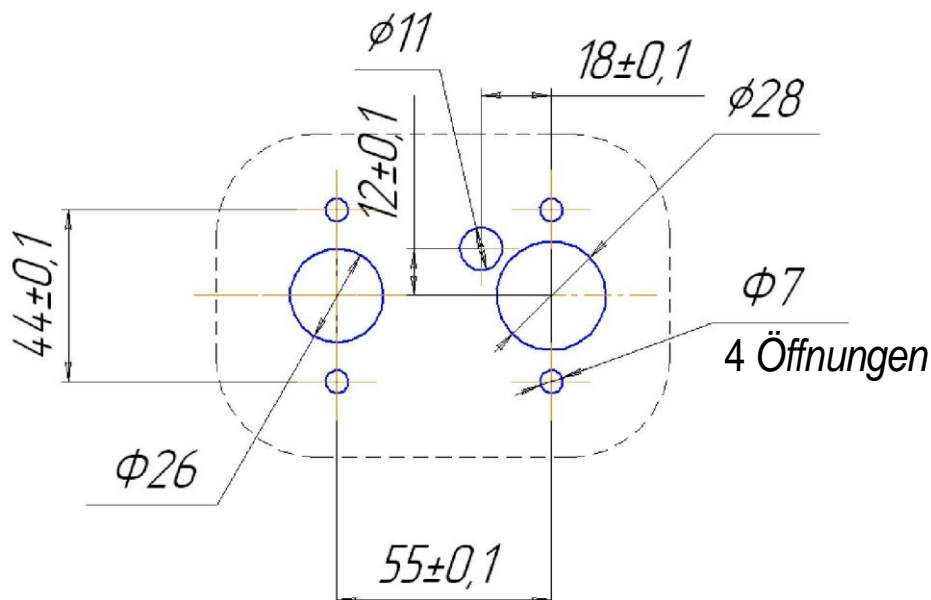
Montageöffnungen für die Installation des Brenners
